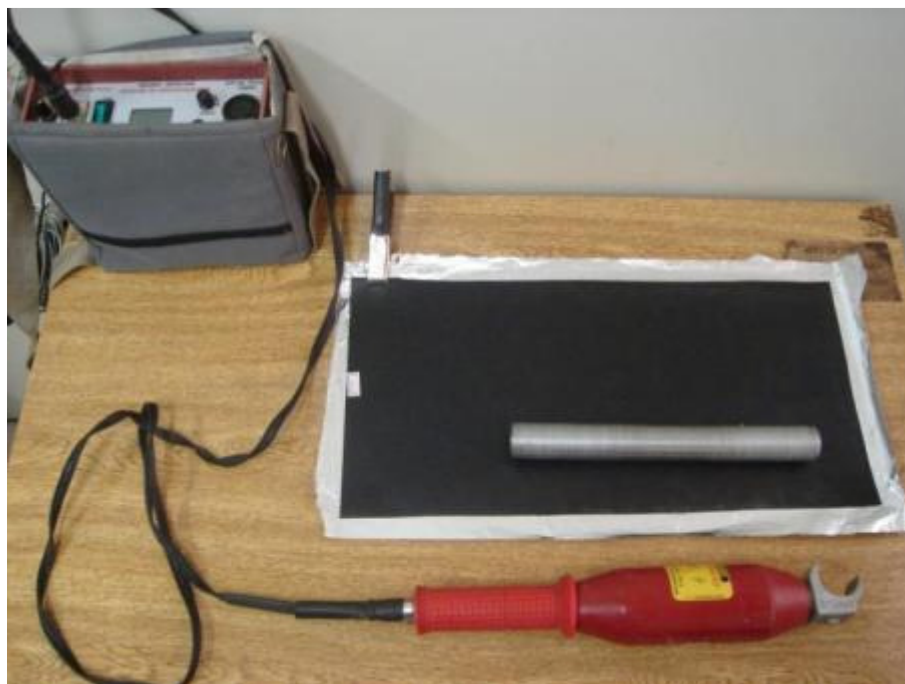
Equipamentos utilizados para determinação de perfurações (*Spark Test*).
